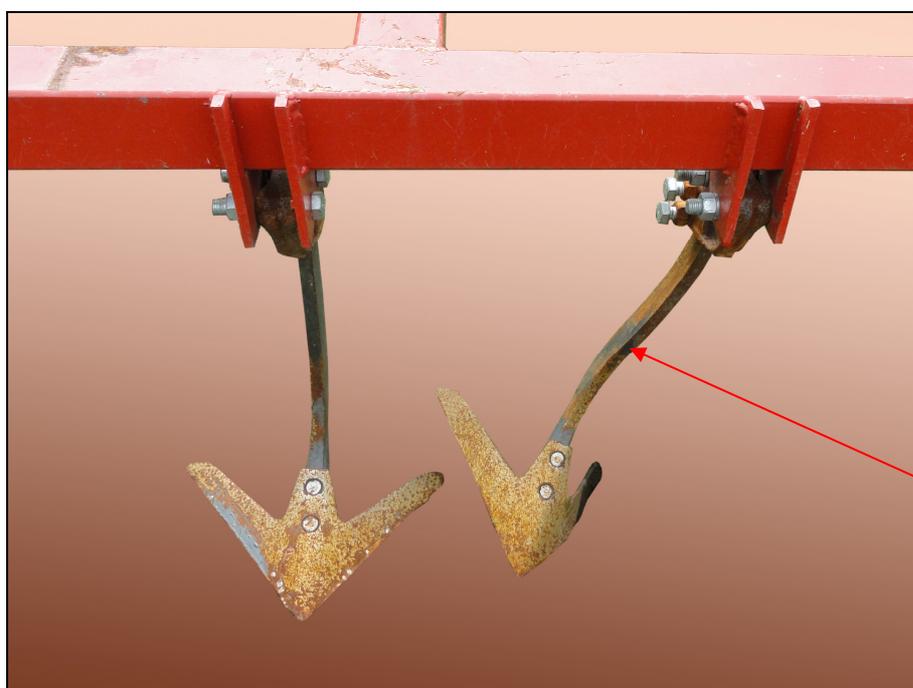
Изгиб стойки крепления стрельчатой лапы
